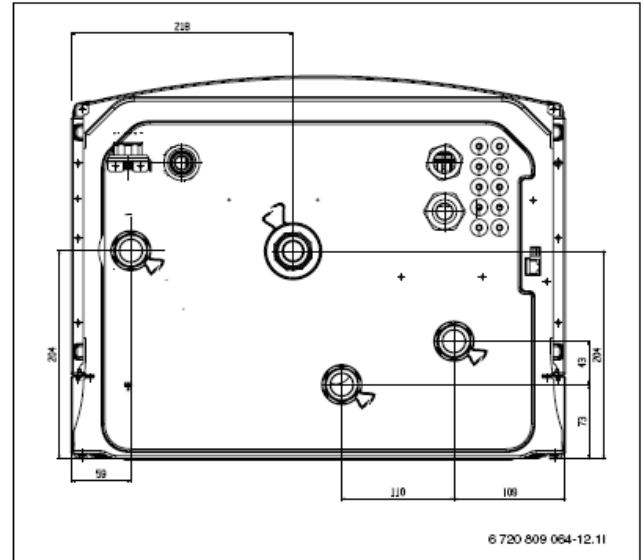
Внутренний настенный блок WPL ... AR-E, габаритные размеры в мм (вид снизу)
